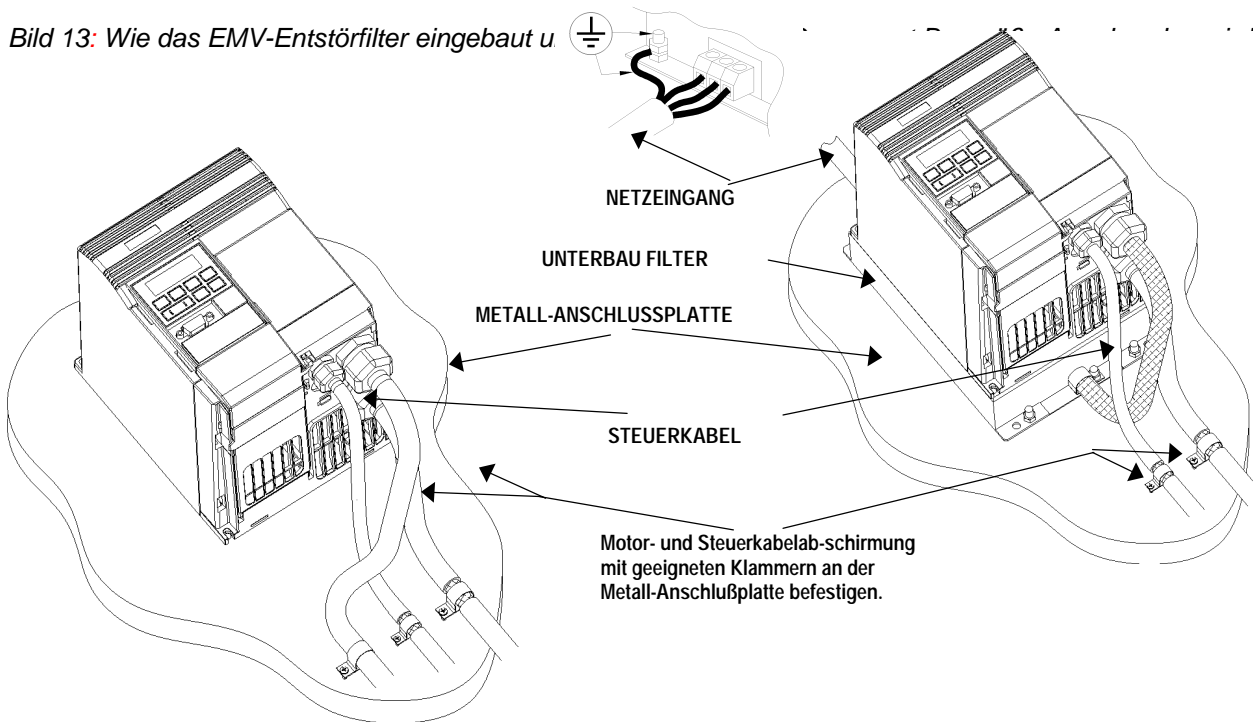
Wie das EMV-Entstörfilter eingebaut und mit dem NORDAC compact Baugröße B verbunden wird.
